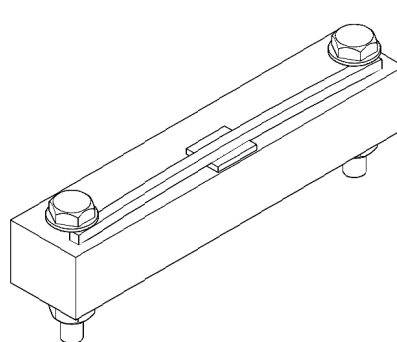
Эскиз образца, установленного в изгибающем устройстве
